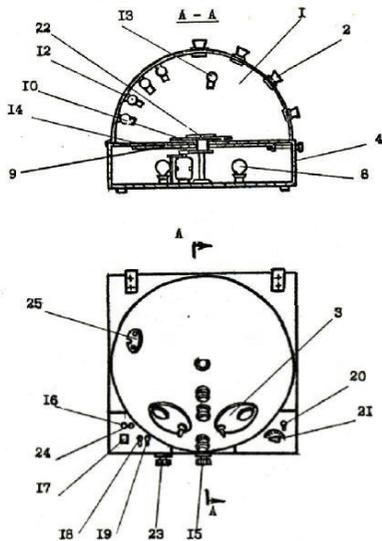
Общий вид полусферической камеры стенда ОТ-8
